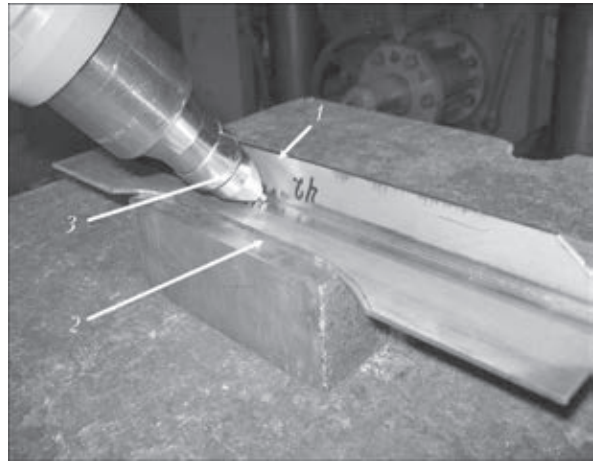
Обработка таврового сварного соединения образца из сплава ВТ20 ручным ударным инструментом по технологии ВМП: 1 — образец; 2 — подкладка; 3 — рабочая головка ударного инструмента
